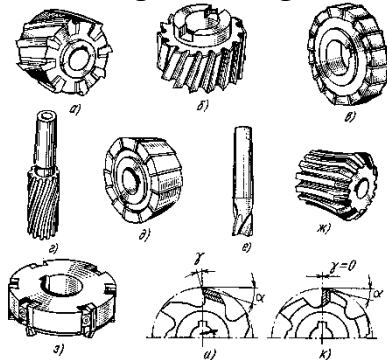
Типы фрез: а – цилиндрическая; б, з – торцовая;
